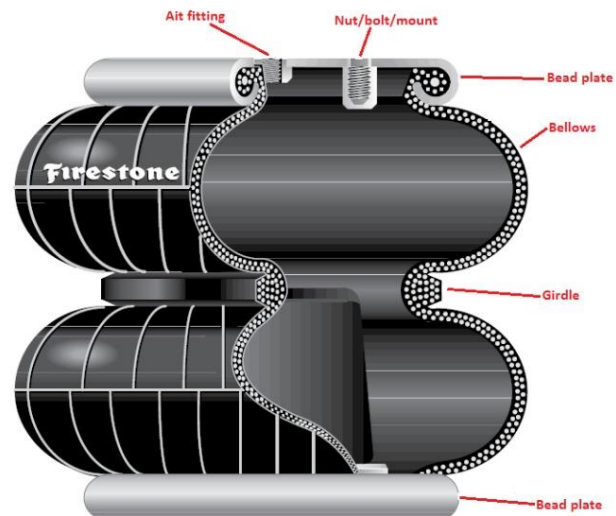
Pieza externa donde se ensambla el Bumper Fuente: Firestone.com.mx
